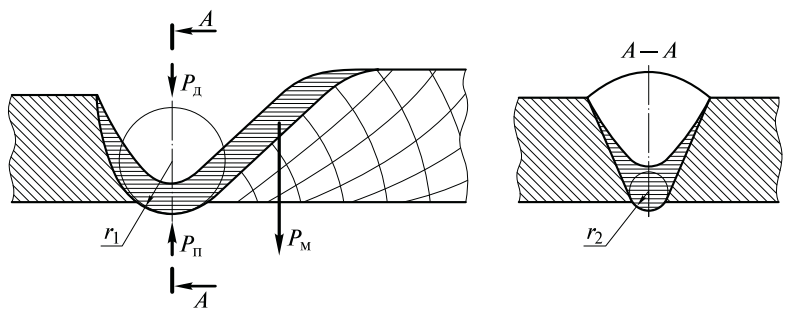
Схема формирования проплава корня сварного шва: P_d — давление дуги; P_M — давление жидкого металла; P_{Π} — сила поверхностного натяжения; r_1 и r_2 — радиусы кривизны ванны в поперечном и продольном направлении
